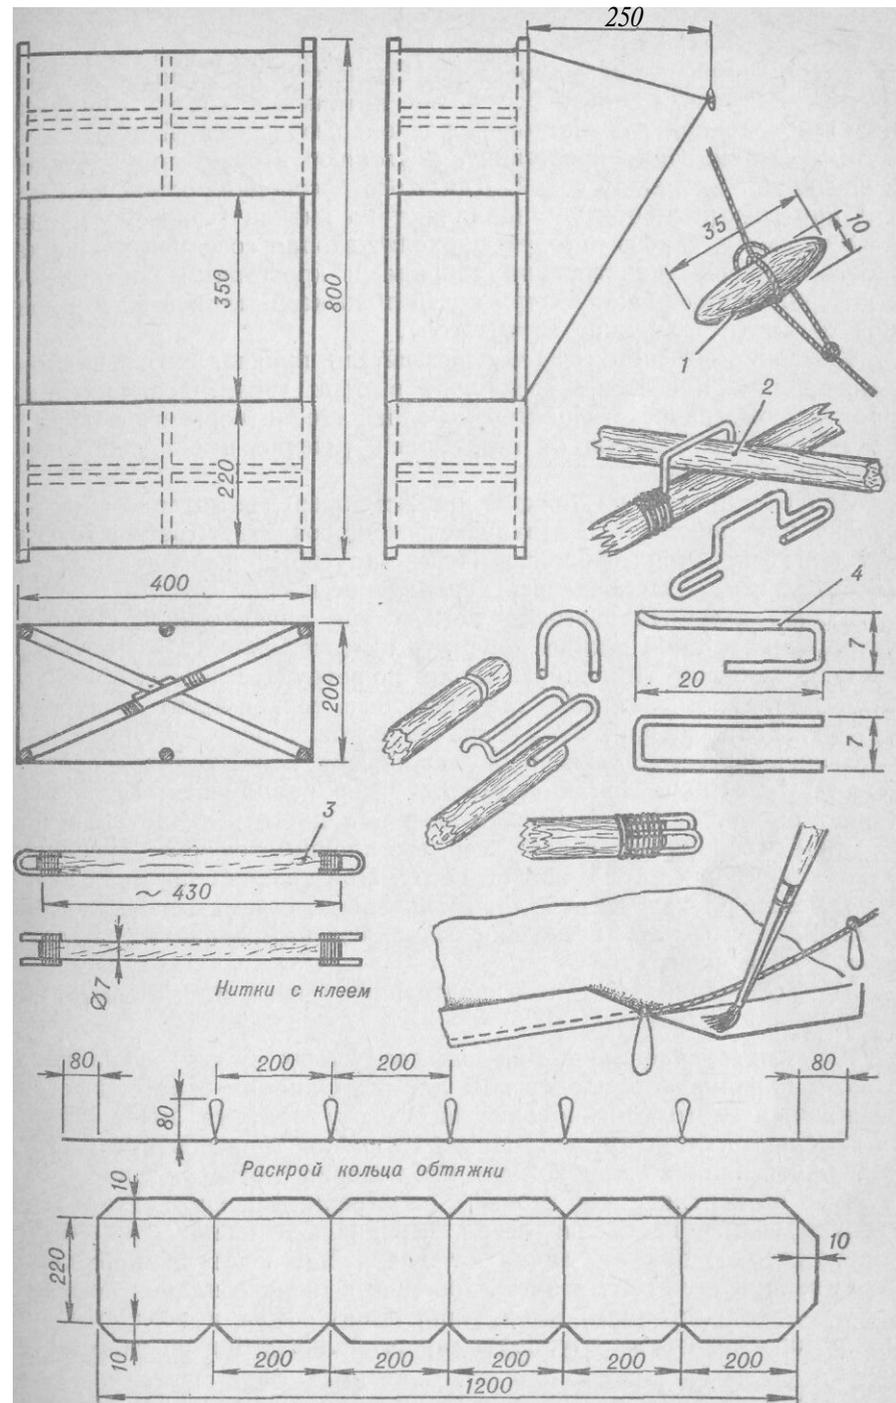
Змей-биплан: / — костыль; 2 — крестовина; 3 — распорная рейка; 4 — концевая вилка
